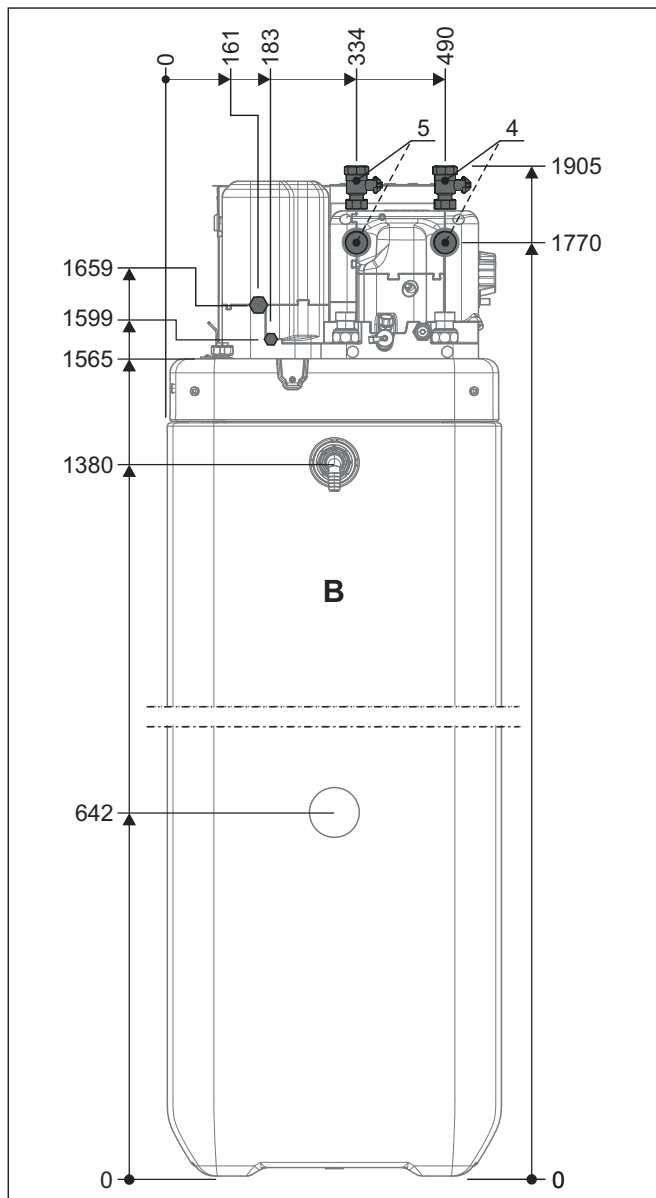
Dimensões vista lateral - ...04P30D/...08P30D
